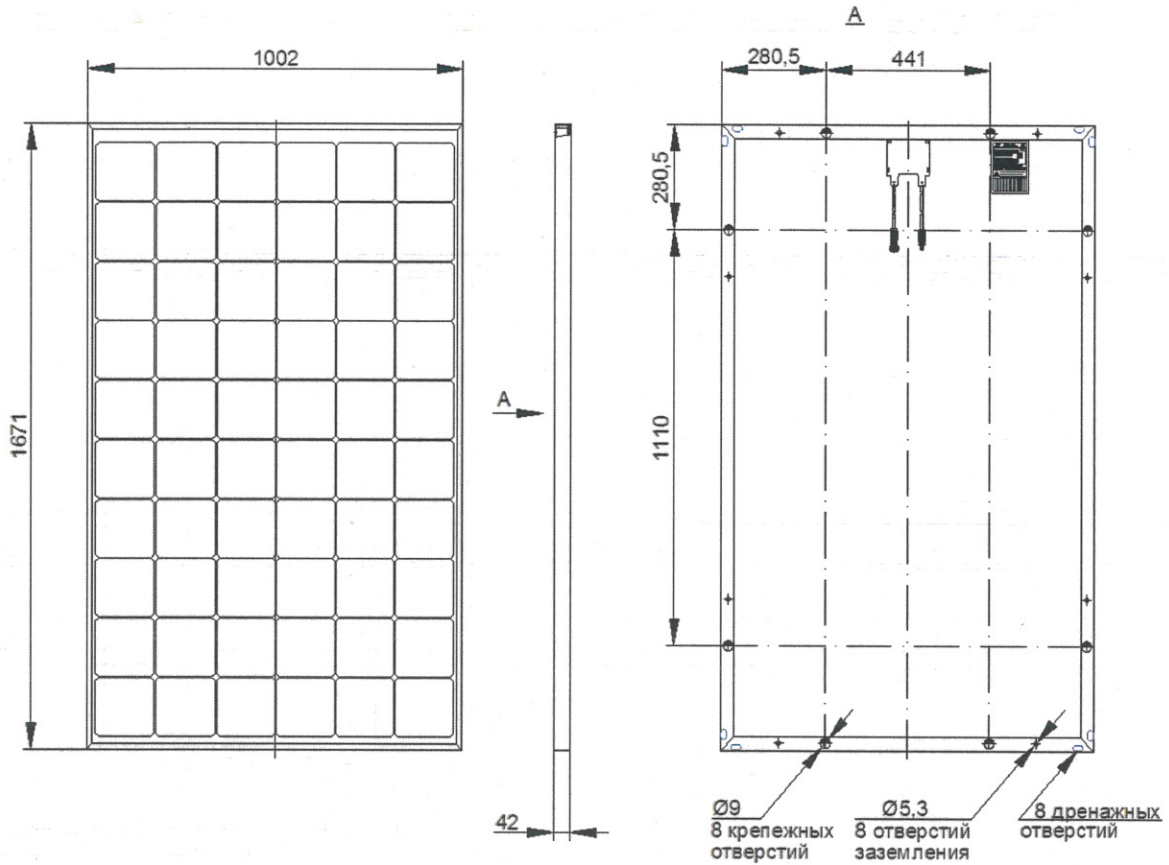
Габаритно-установочные размеры ФЭМ
